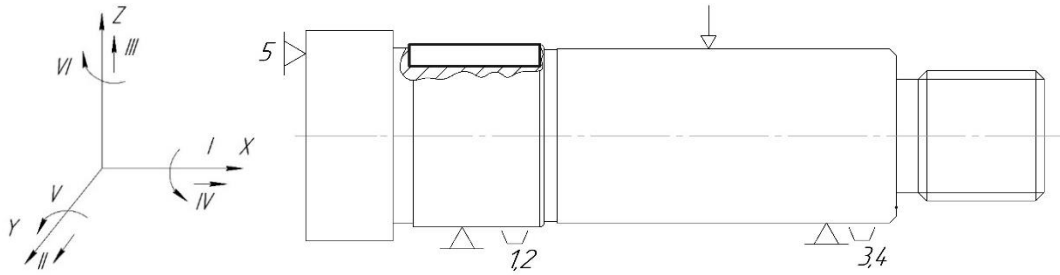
Схема базування, закріплення заготовки при операції 030 «Шпонково-фрезерна»
